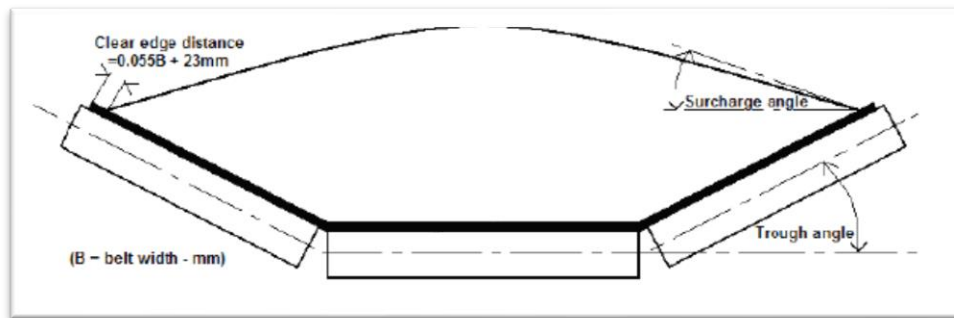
Sección transversal de la banda transportadora. (Fuente: Dunlop Conveyor Handbook)
